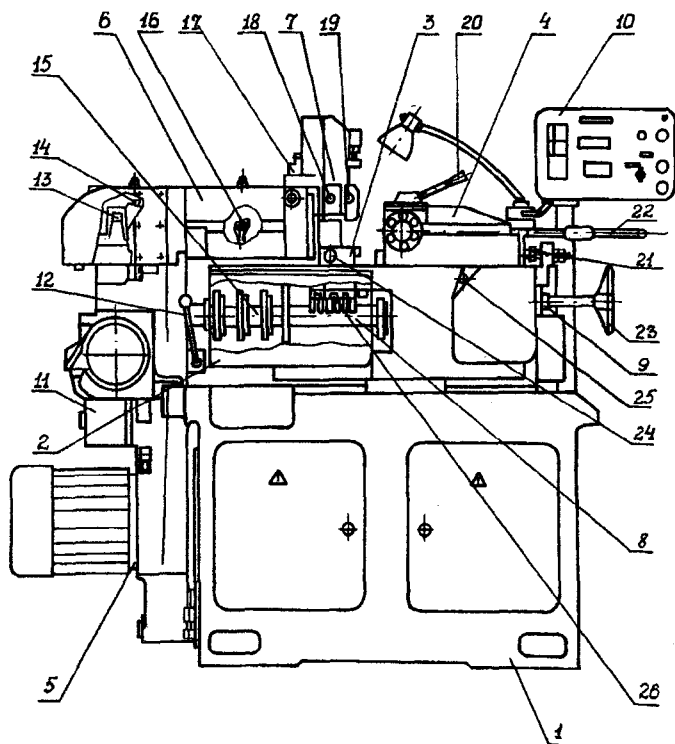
Общий вид токарно-револьверного автомата модели 1М116
